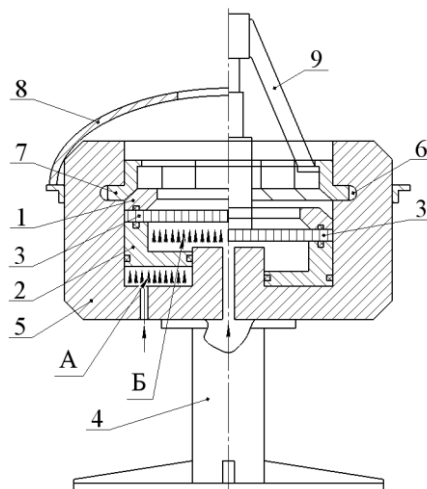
Силовой блок установок типа УДИ для испытания сварных соединений при двухосном изгибе: 1 — матрица;
